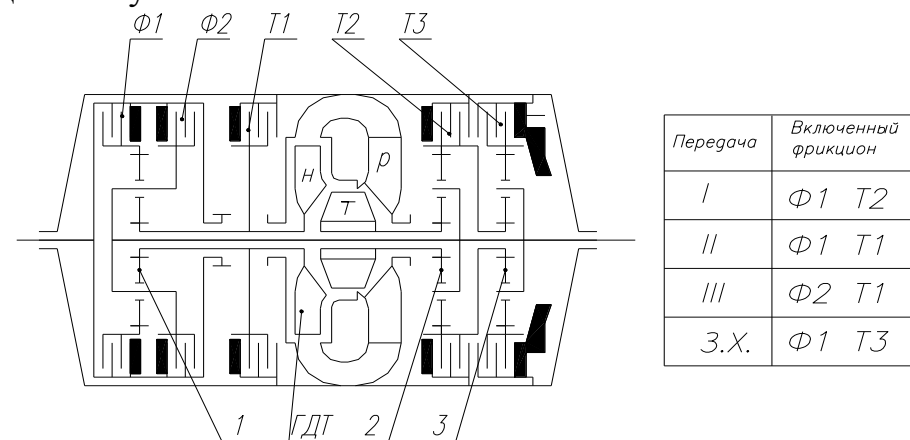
Кинематическая схема двухпоточной гидромеханической передачи
